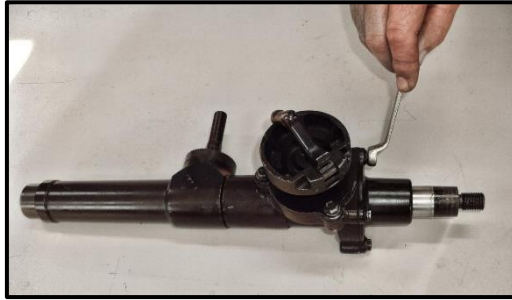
Desenroscamento dos parafusos da tampa superior da caixa de engrenagem
